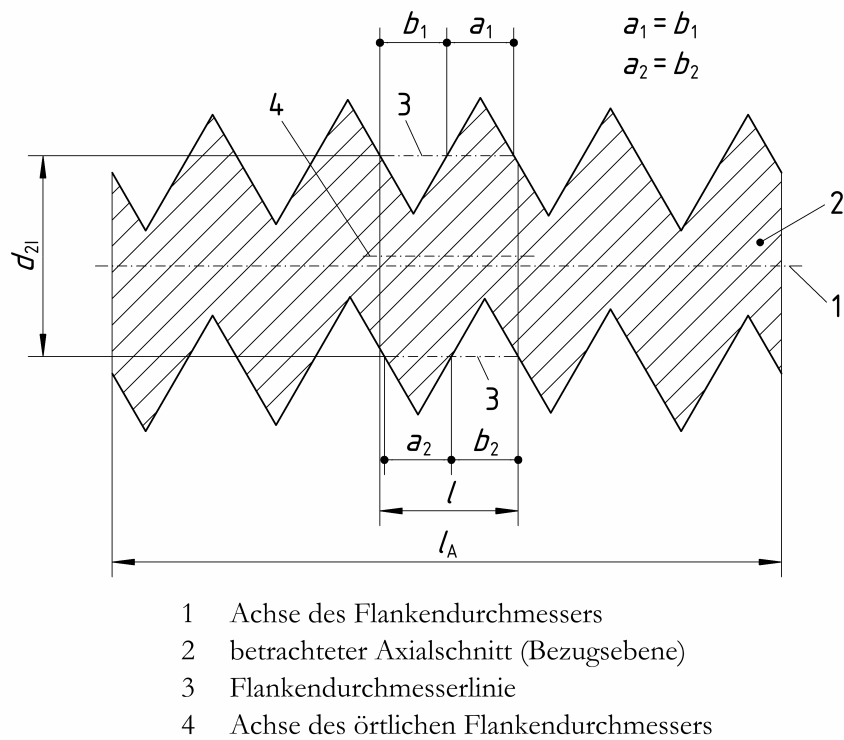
Flankendurchmesser eines zylindrischen eingängigen Außengewindes
